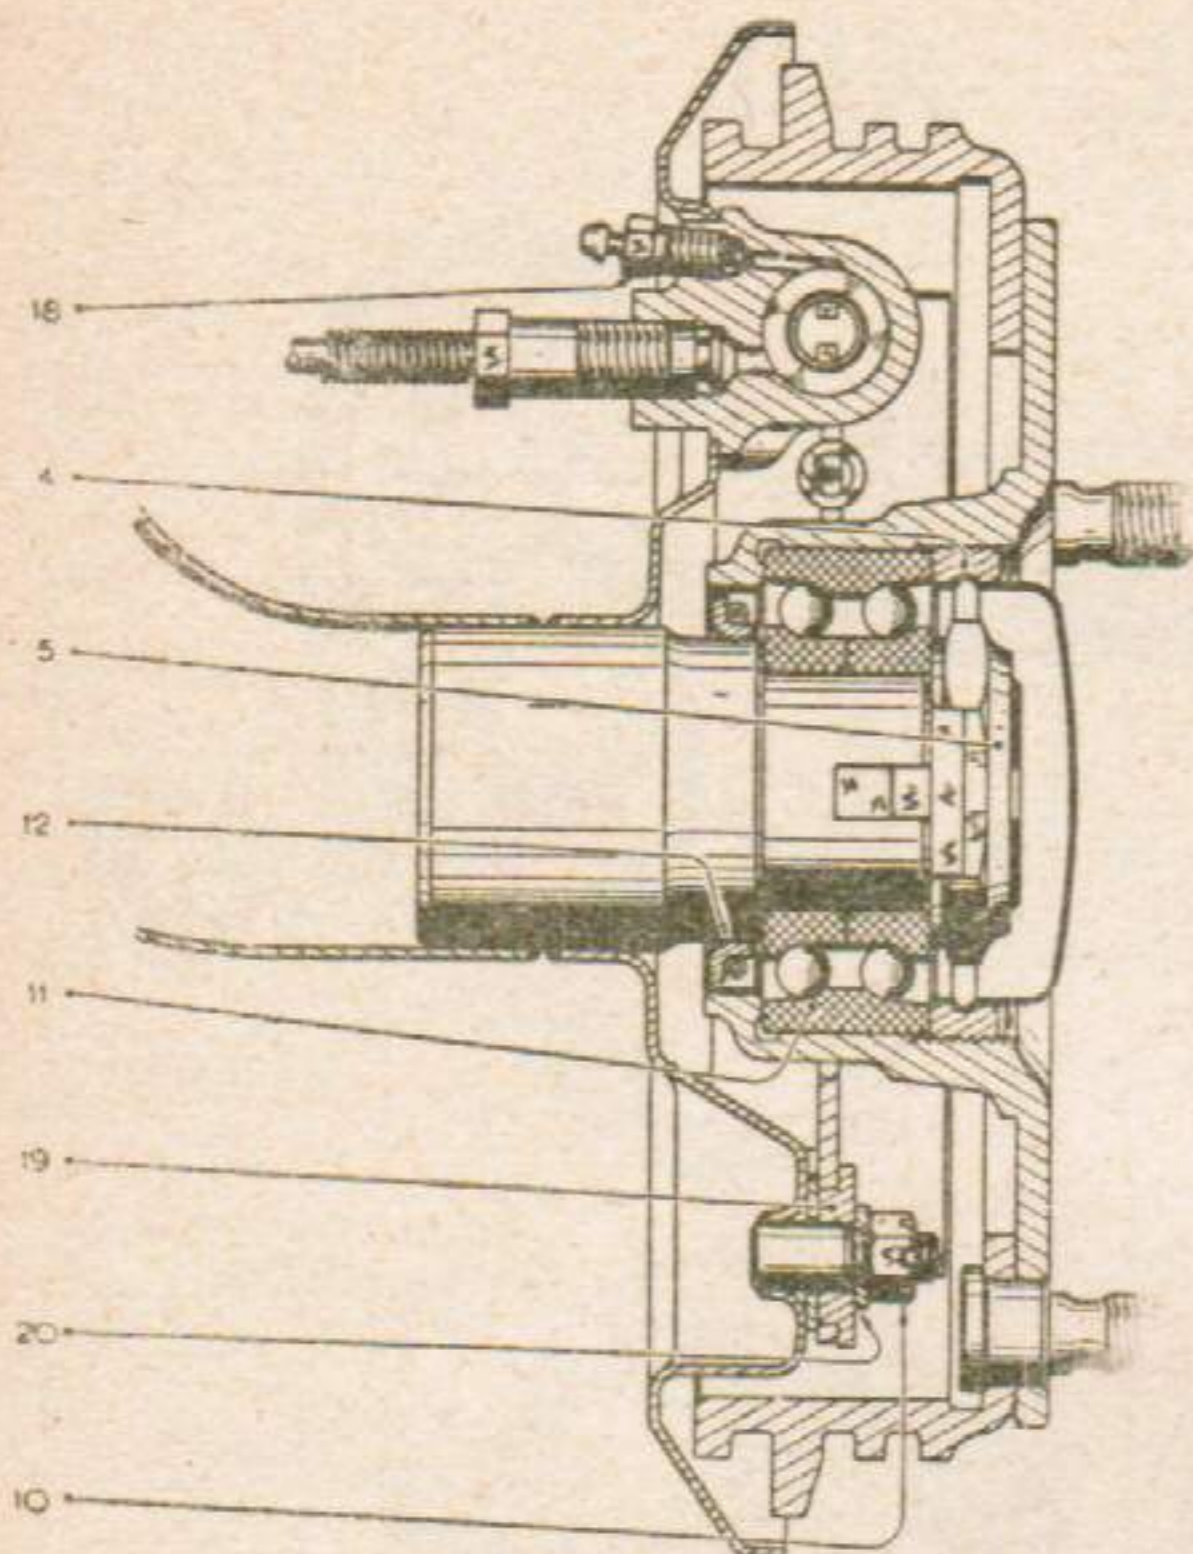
Vue en coupe d'un moyeu tambour arrière.
